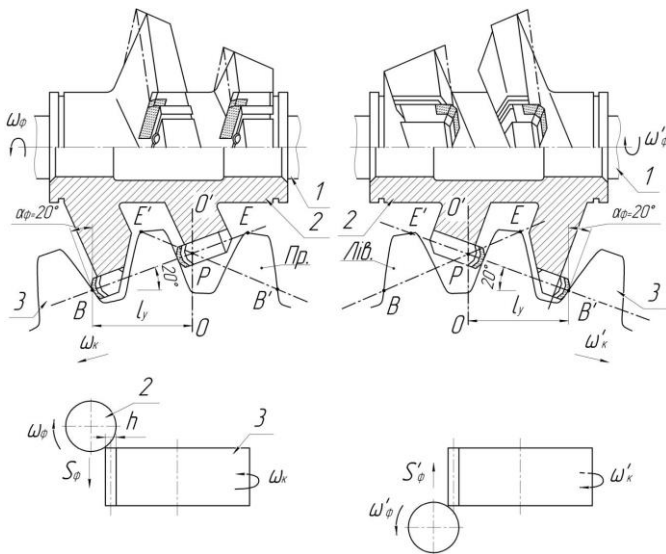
Схема оброблення зубів колеса одним правим корпусом фрези: а), с) – правий корпус при зустрічному фрезеруванні; б), d) - правий корпус при попутному фрезеруванні
